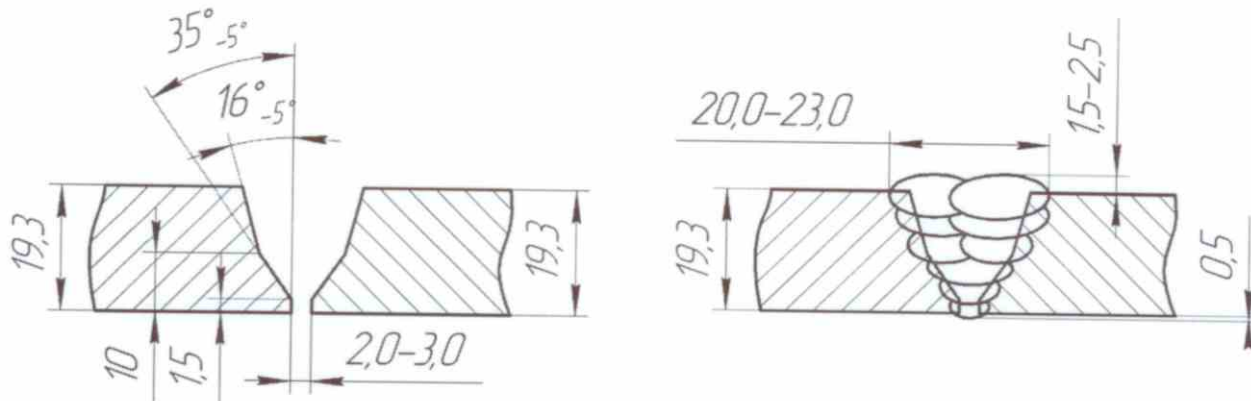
Геометрические параметры сборки и сварного шва
